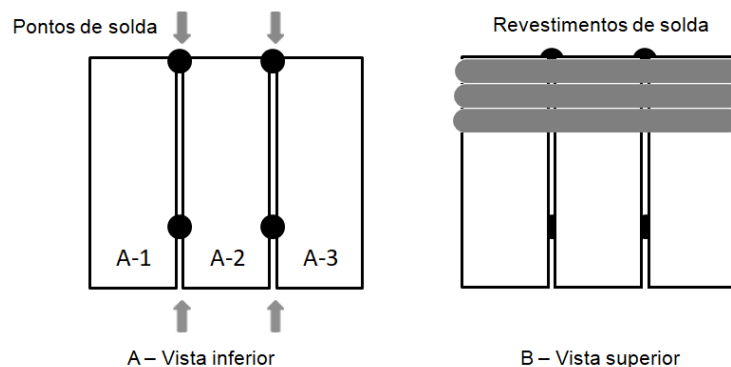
Desenho esquemático da união dos corpos de prova (A) e do revestimento de solda (B)
